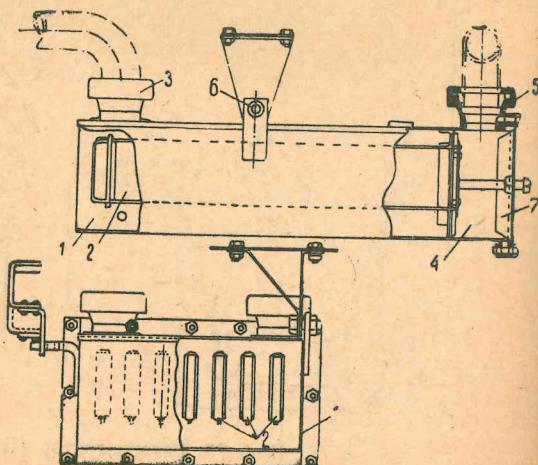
Газоочиститель установки ЦНИИМЭ-5
